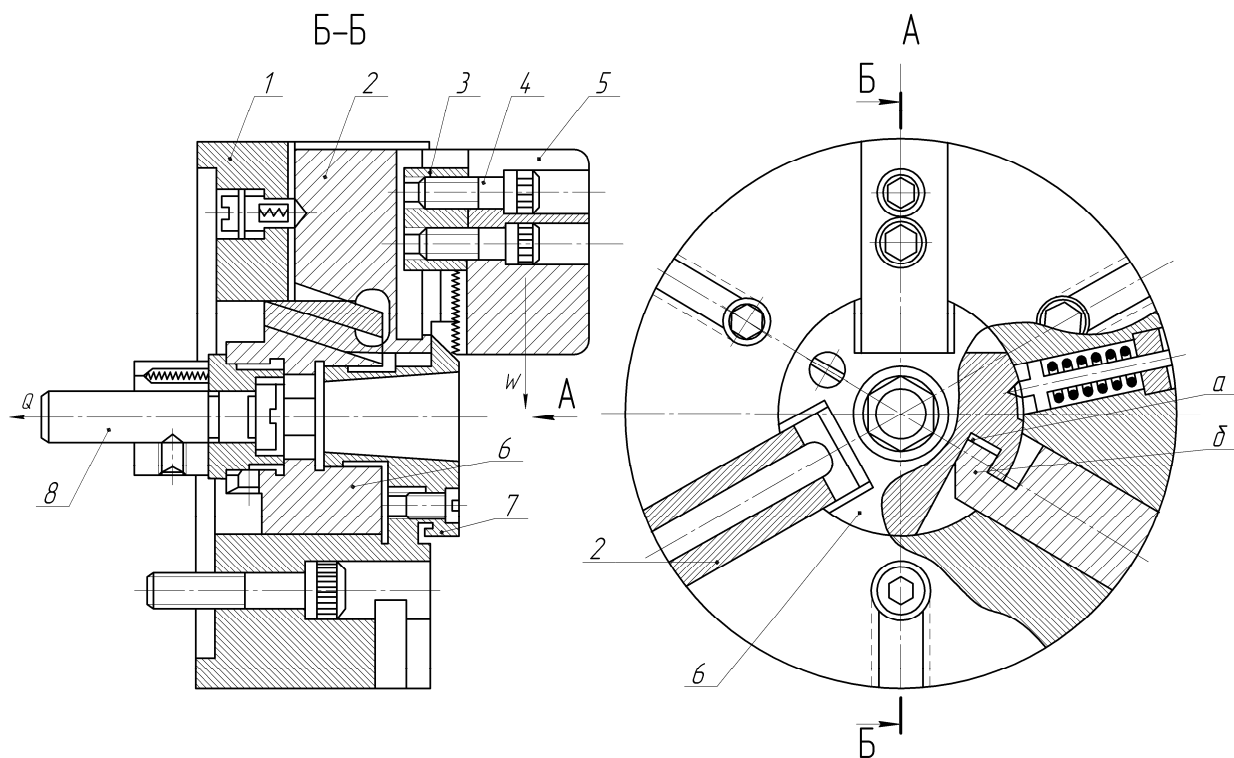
Будова й параметри клинового токарного трикулачкового патрона з механізованим приводом: 1 – корпус; 2 – кулачок; 3 – сухар; 4 – гвинт; 5 – змінний кулачок; 6, 7 – втулки; 8 – тяга; A – вид спереду з виступом кулачка 2; $B-B$ – переріз; Q – осьова сила на штоку механізованого приводу; W – сила затискача кулачка патрона
